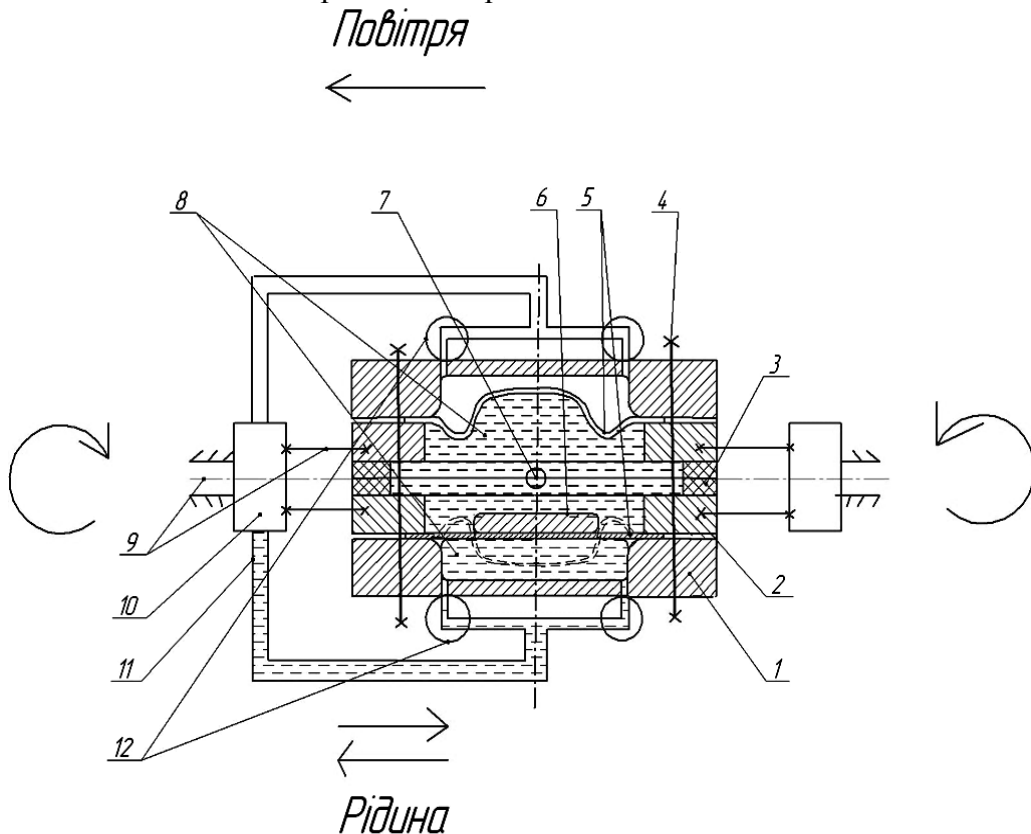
Схема пристрою для штампування коробчастих деталей імпульсними джерелами енергії.
